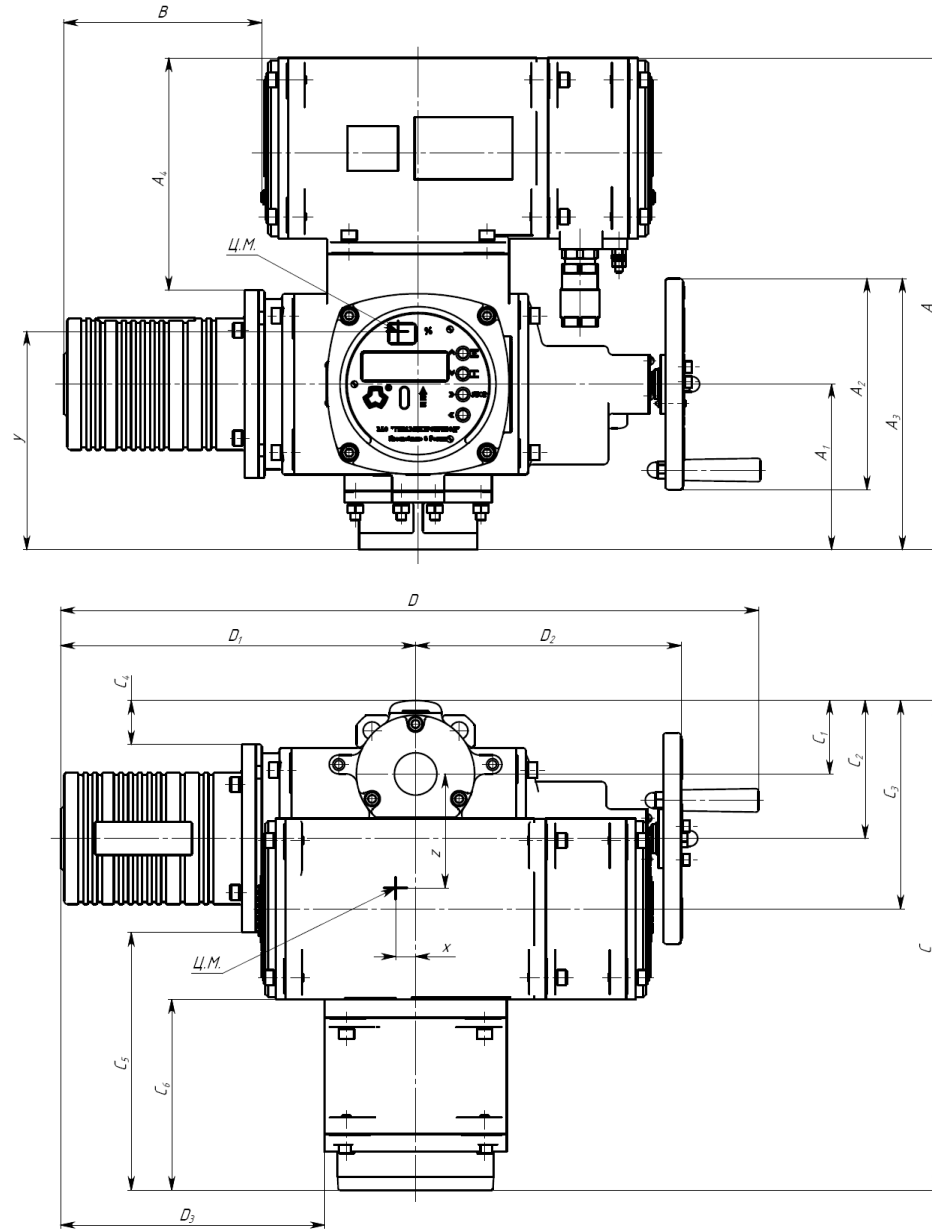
д – Габаритные размеры привода конструктивной схемы 40
